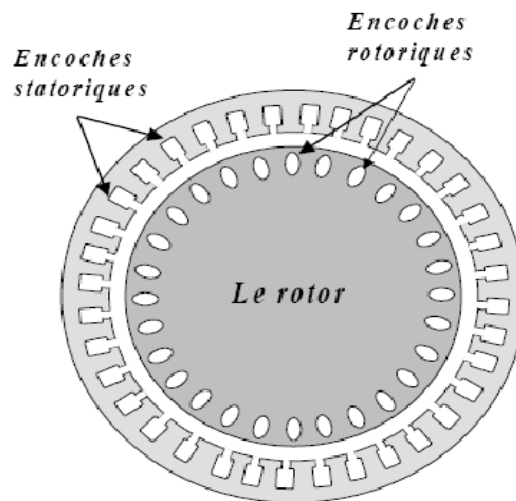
Rotor à cage d'écureuil [NOU21]
